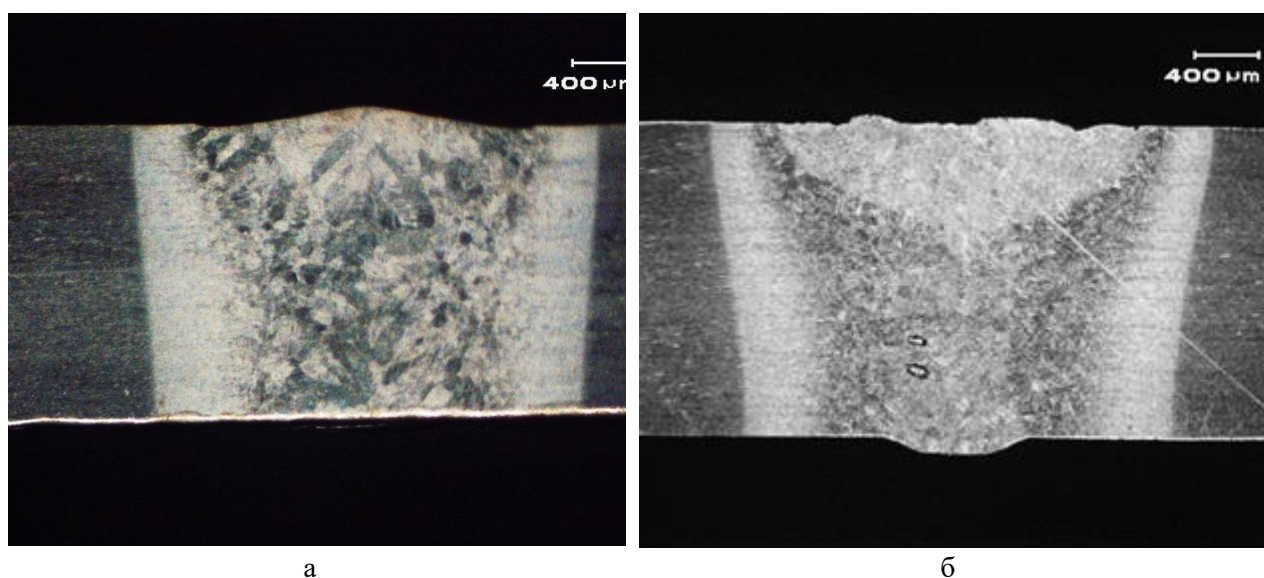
Макрошлифы полученных образцов: а) режим - сварка с использованием защитного газа; б) режим 3 - без защитного газа.
